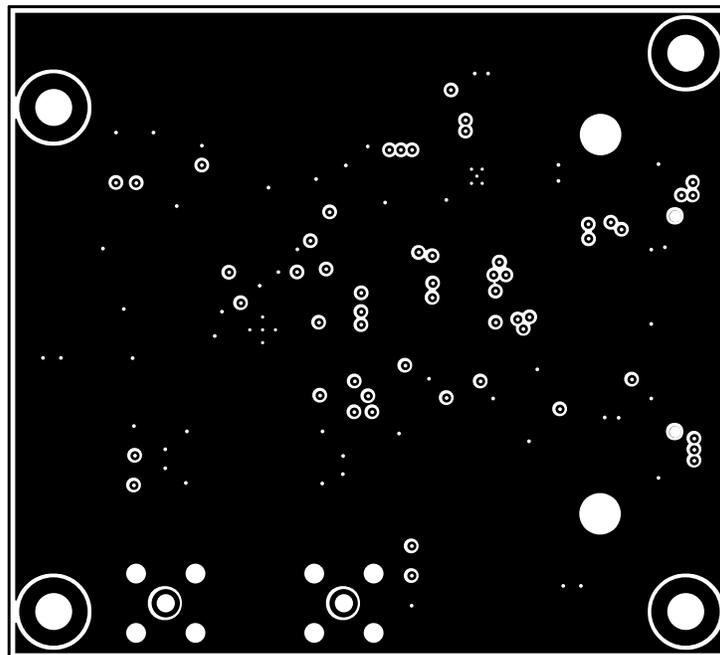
ADS8681WEVM PCB 第 2 层 - GND 平面
